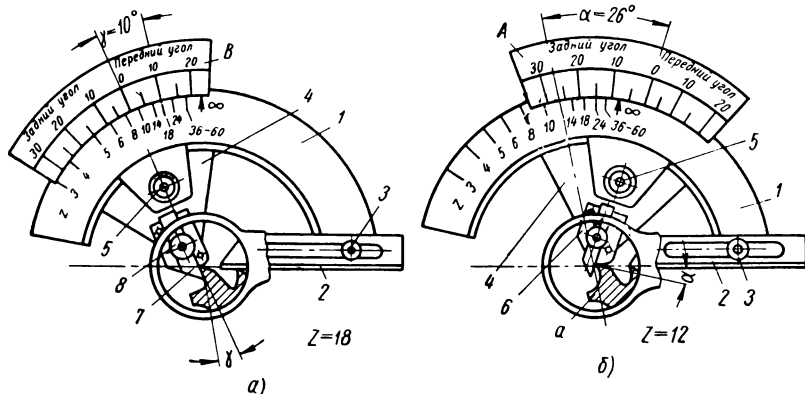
Установка угломера М. И. Бабчиничера для измерения:
